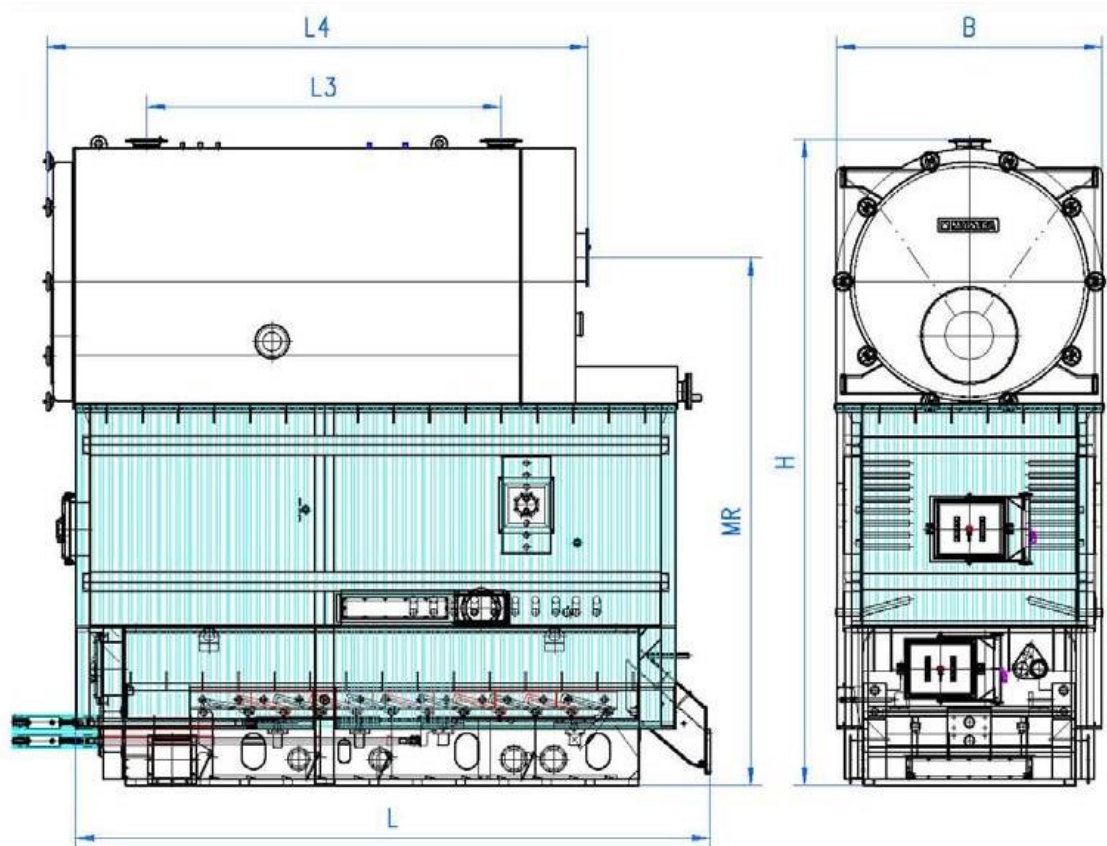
Схема котла MAWERA FSR 3300 [3]
